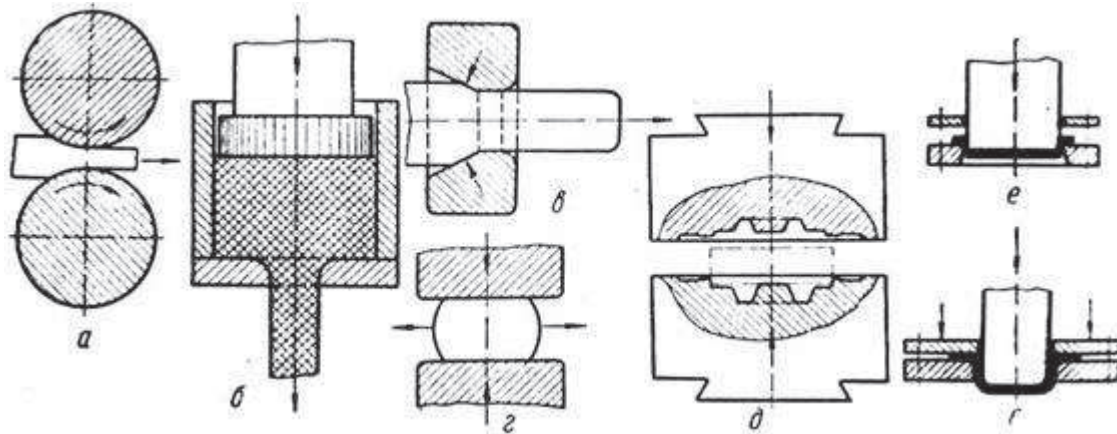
Основні способи обробки тиском (а,г - прокатування; б - олочіння; в - пресування; д - вільне кування; е,ж - листове штампування)
